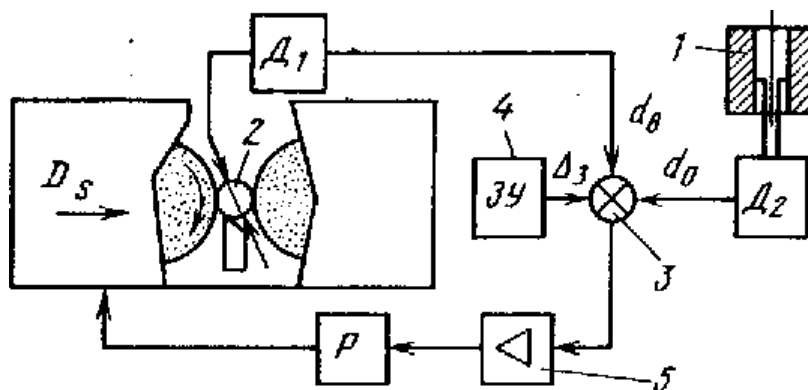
Схема сборки автоматической пригонкой плунжеров под размер втулки [13]
